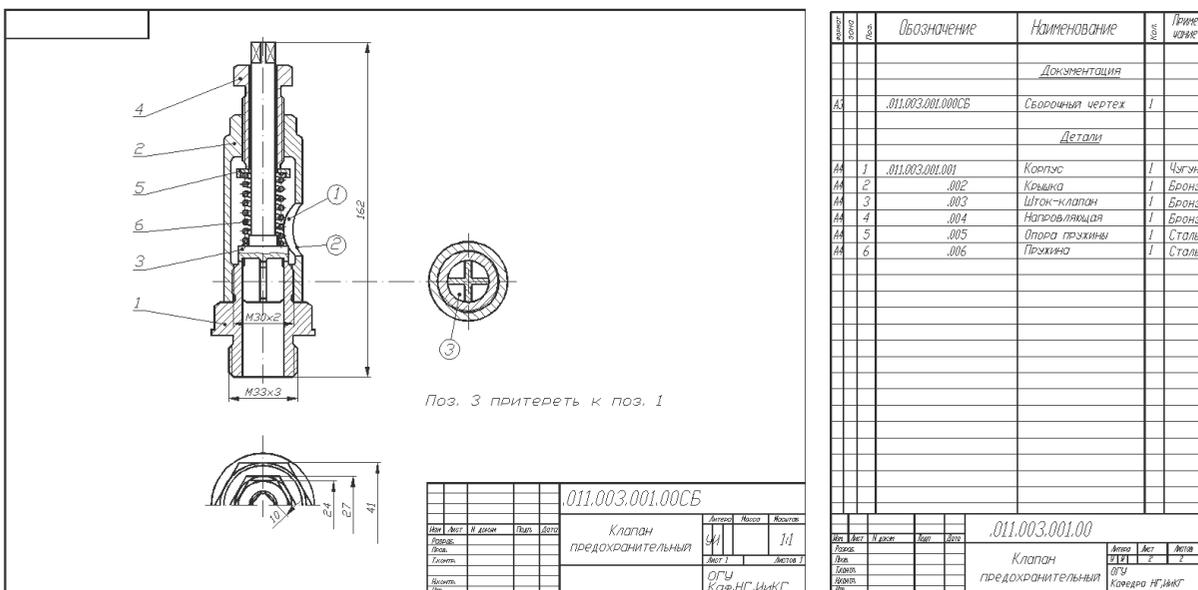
Пример 2D-модели сборки (сборочного чертежа) «Клапан предохранительный» со спецификацией
